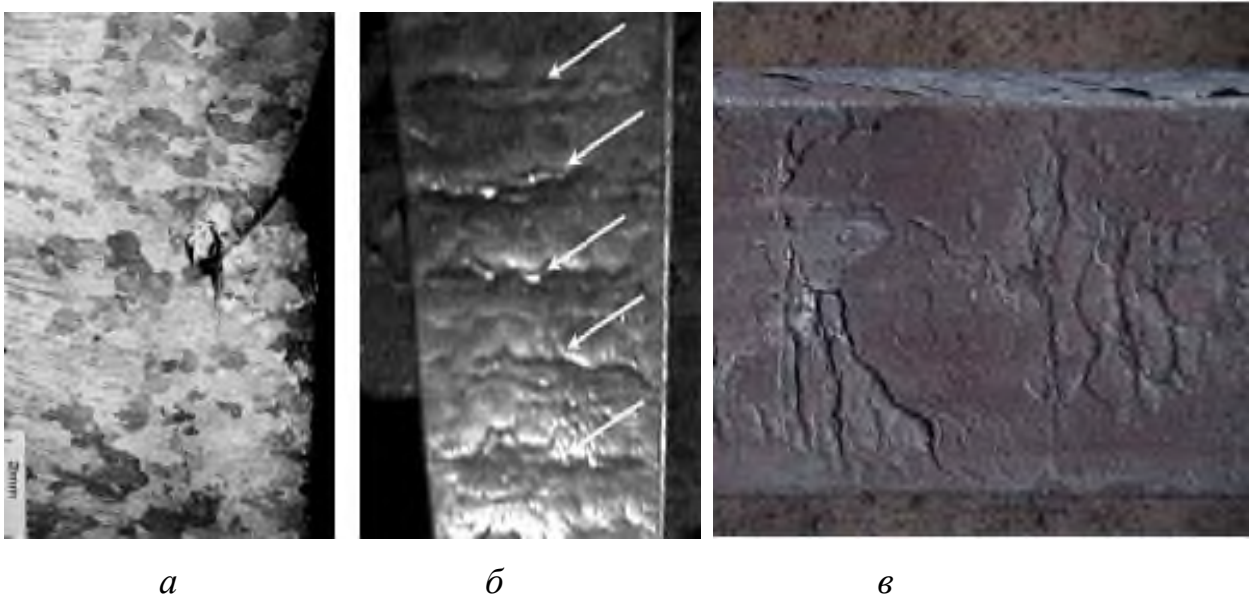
Поздовжній перетин зразка безперервнолитої заготовки в місці розташування залівін (а) та її фото на поверхні заготовок (б, в)
